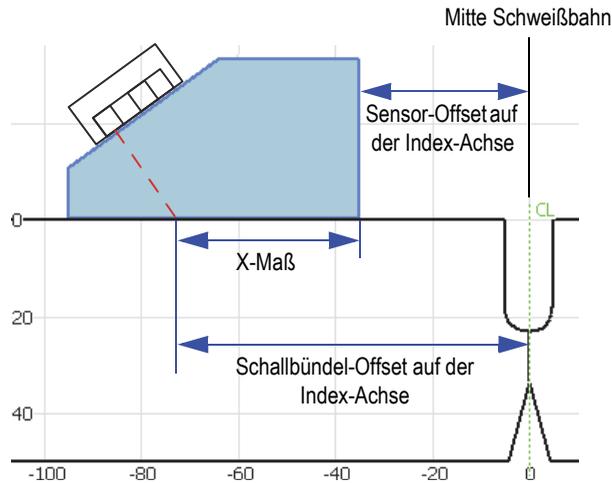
Schallbündel-Offset auf der Index-Achse bei der Schweißnahtprüfung
